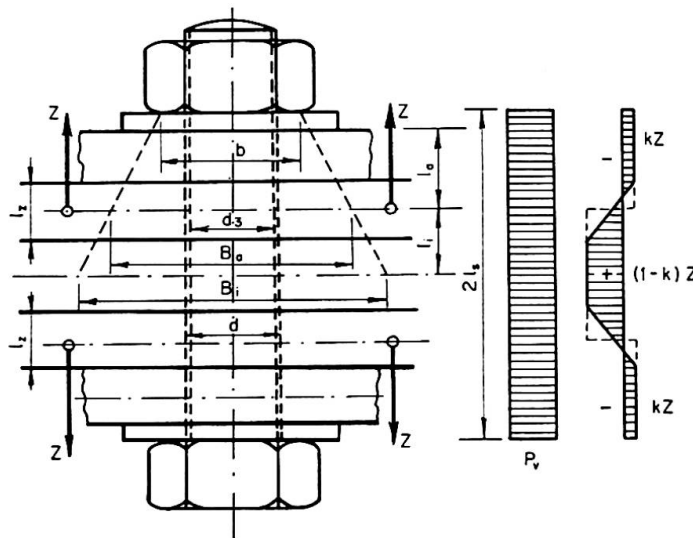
Berechnung von zugbeanspruchten Schrauben.
